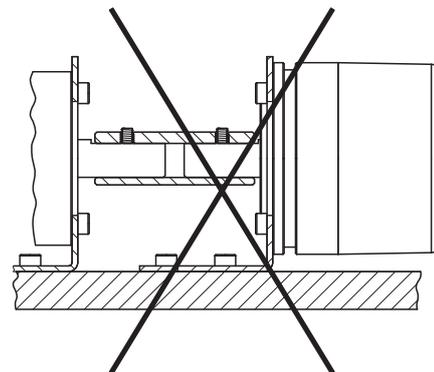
Montageansicht – nicht an Wellen und Flanschen gleichzeitig starr verbinden
